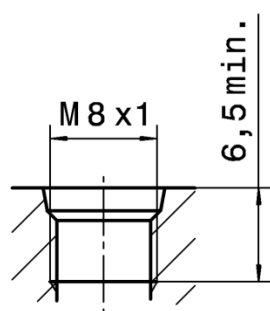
Formbohrung für Gewinde M 8 x 1 (203^N)
